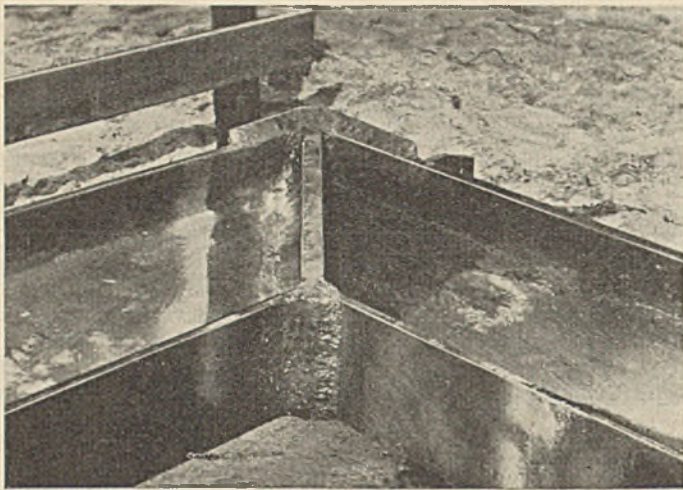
Gasgeschweißte Rahmenecke.
